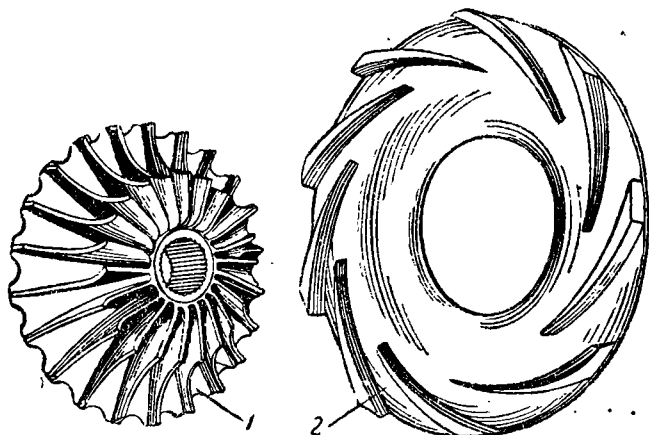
Ротор центробежного компрессора ТРД РД-500.
